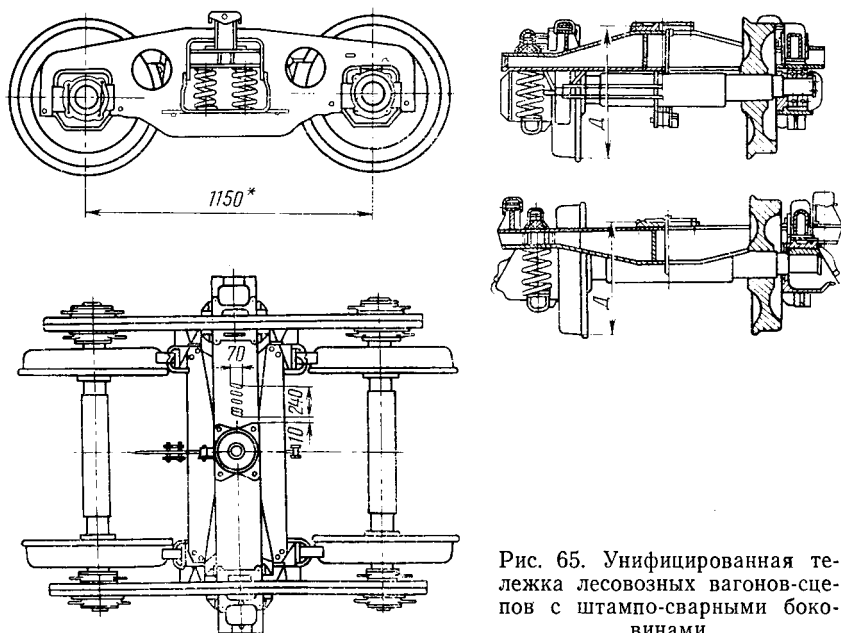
Унифицированная тележка лесовозных вагонов-сцепов с штампо-сварными боковинами
